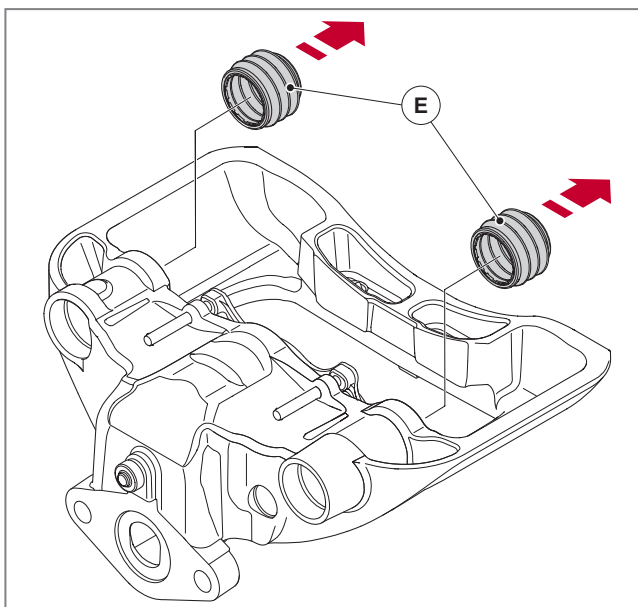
Faltenbälge und Führungsbolzen entfernen
